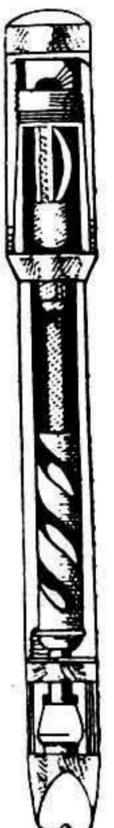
Coupe d'un stylographe à plume rentrante (Safety).
